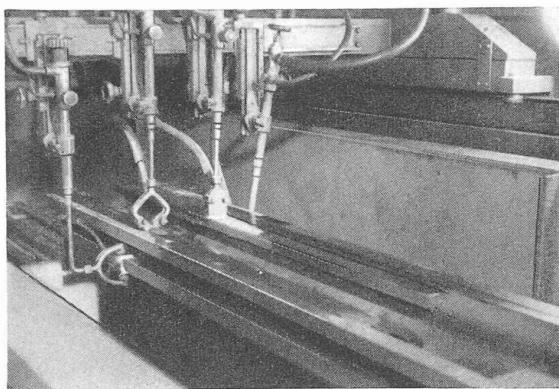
Trempe de guidages sur machine à tremper les coulisses de tour.
